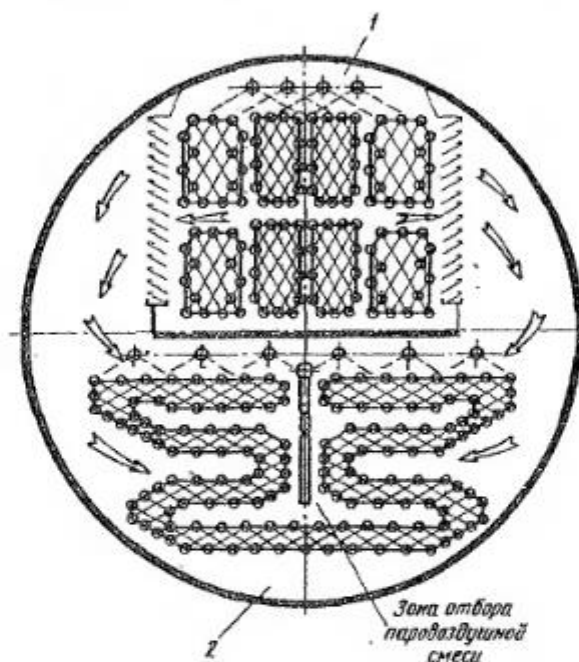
Конструктивная схема блока абсорбер-испаритель:
